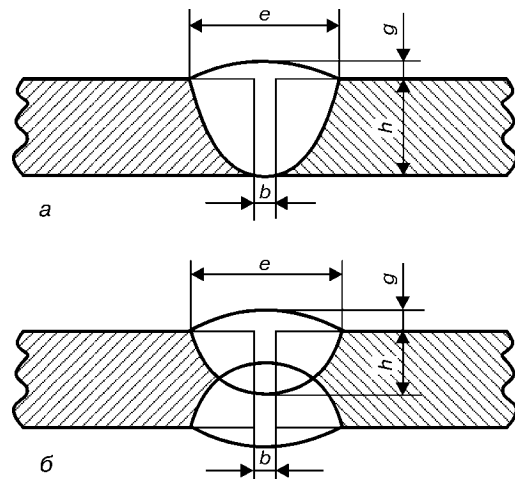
Размеры шва стыкового соединения без скоса кромок: а — односторонний шов; б — двусторонний
